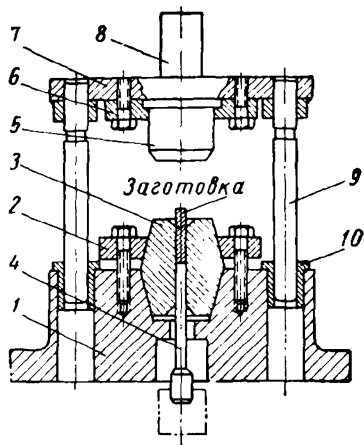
Штамп со сменными рабочими деталями для поковки стержневого типа: 1 — нижняя плита; 2 — зажимная планка матрицы; 3 — матрица (сменная); 4 — выталкивающая шпилька; 5 — пуансон (сменный); 6 — зажимная планка пуансона; 7 — верхняя плита; 8 — хвостовик; 9 — направляющая колонка; 10 — направляющая втулка
